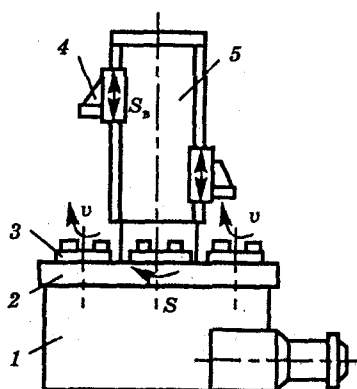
Токарный вертикальный многшпиндельный полуавтомат роторной обработки
